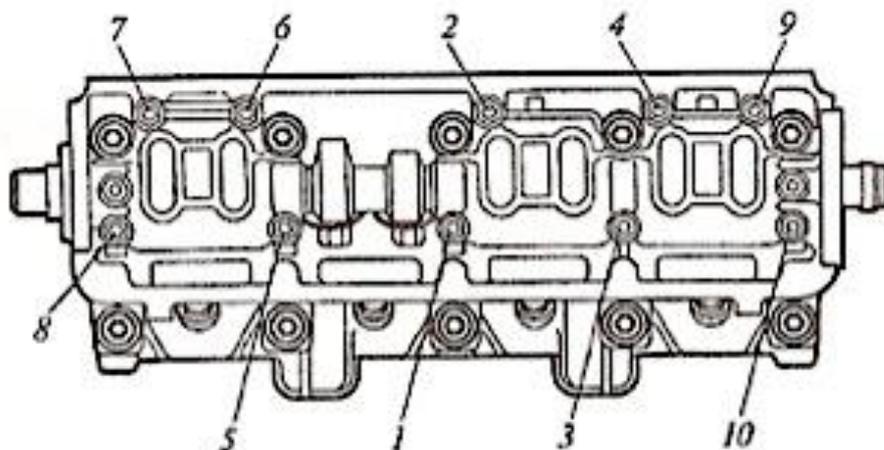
Порядок затягивания гаек крепления корпусов подшипников распределительного вала
